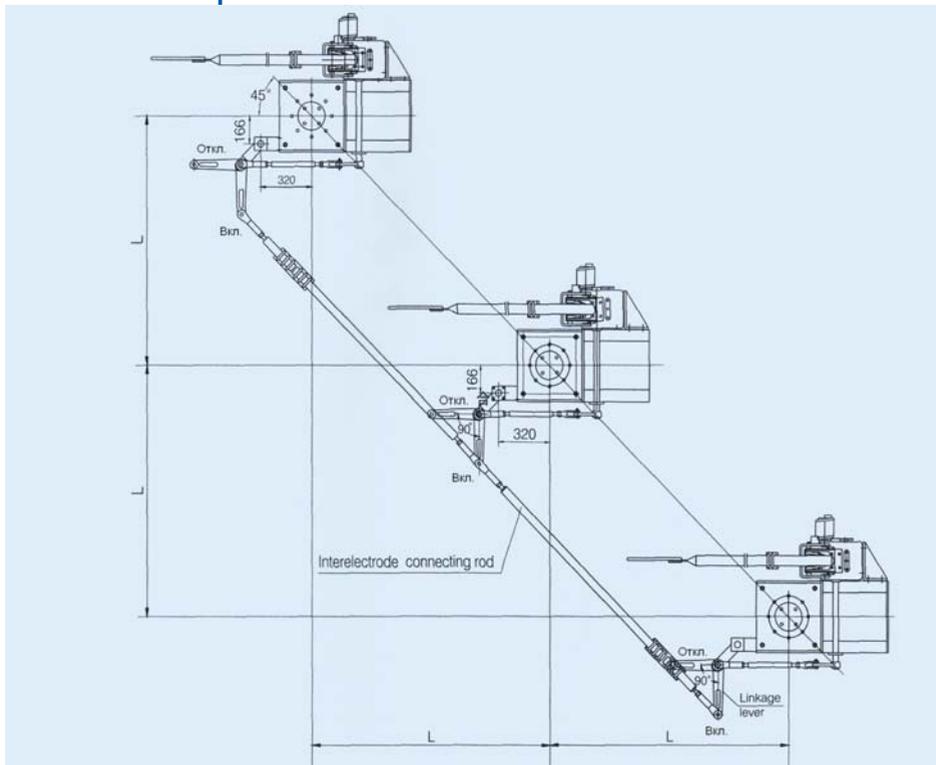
Внешний вид и размеры заземлителя JW□-252
